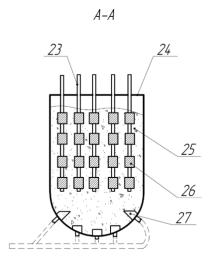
Форма сечения резервуара вибростанка согласно схеме рис. 3
